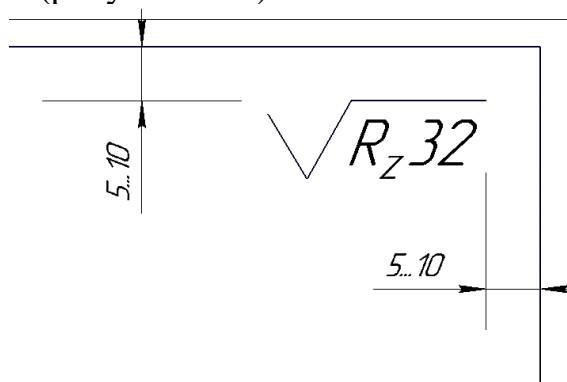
Обозначение одинаковой шероховатости для всех поверхностей
